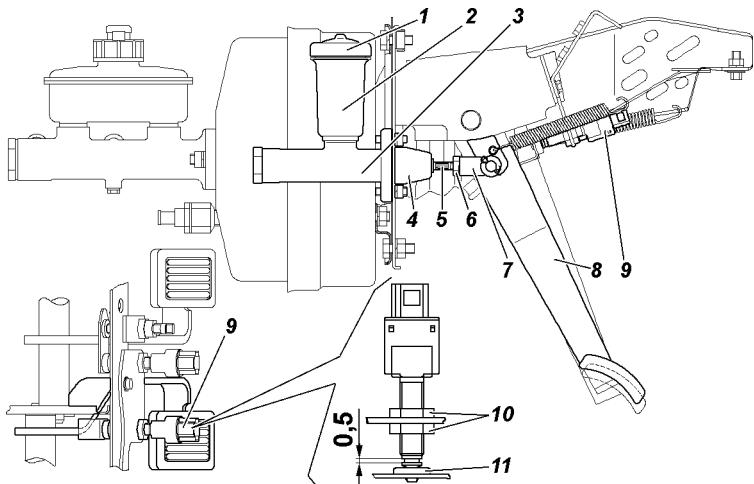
Привод главного цилиндра выключения сцепления:
